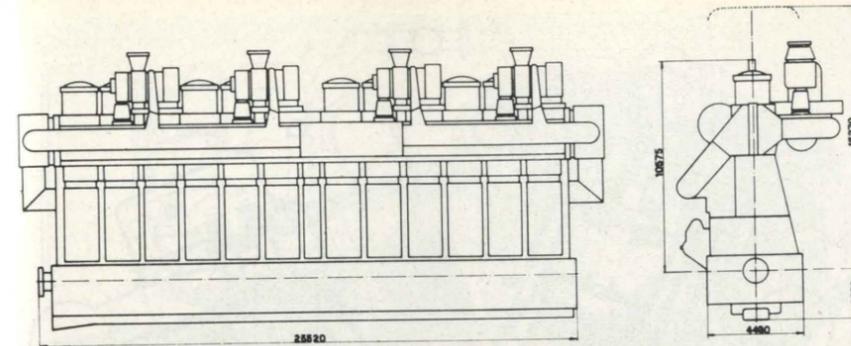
Motore Diesel da 40.000 Cv a 102 giri/min. (12 cilindri diam. 1060 mm - corsa 1900 mm).
